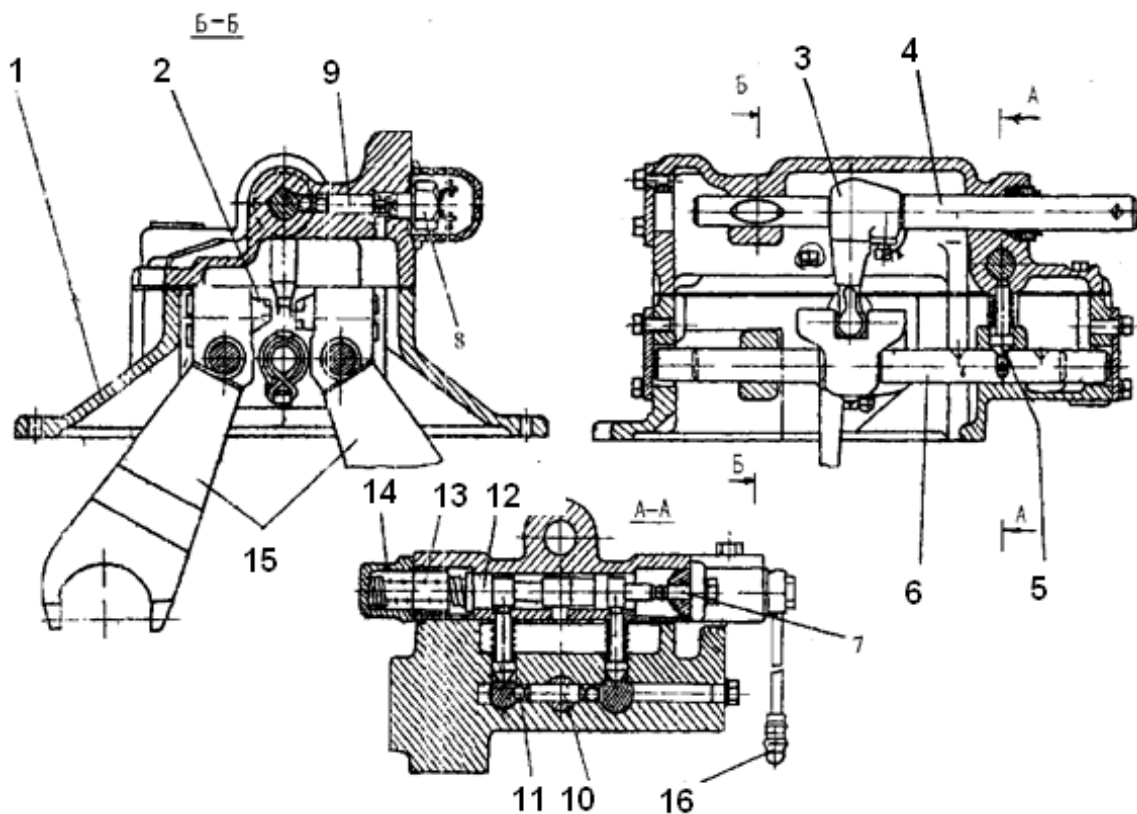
Механизм переключения диапазонов: 1 – корпус; 2 – разделитель; 3 – рычаг; 4 – шток управления; 5 – фиксатор; 6 – шток переключения диапазонов; 7 – шток гидроцилиндра блокировки; 8 – выключатель блокировки запуска двигателя; 9 – толкатель; 10 – палец блокировки; 11 – шарик блокировки штоков; 12 – шток блокировки самовыключения диапазонов; 13 – пружина; 14 – крышка; 15 – вилки переключения диапазонов; 16 – клапан
